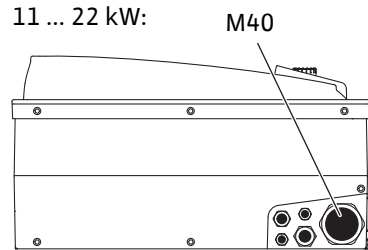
Kabelverschraubungen für Netzanschlusskabel
